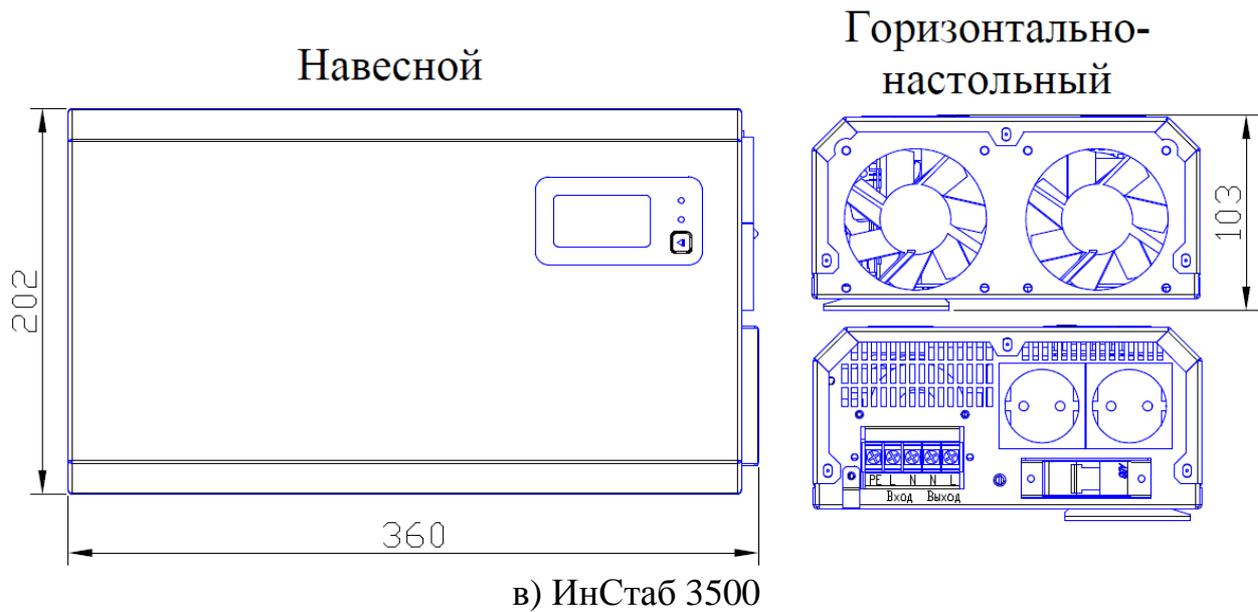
Габаритные размеры стабилизатора Штиль и рекомендуемые варианты установки
